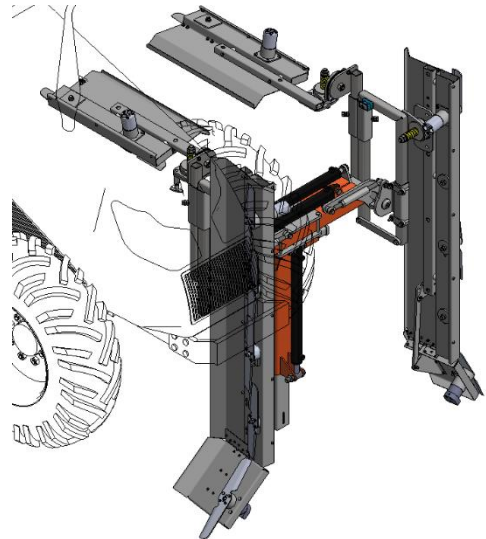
Ex. módulos de corte horizontais na posição de "repouso"
